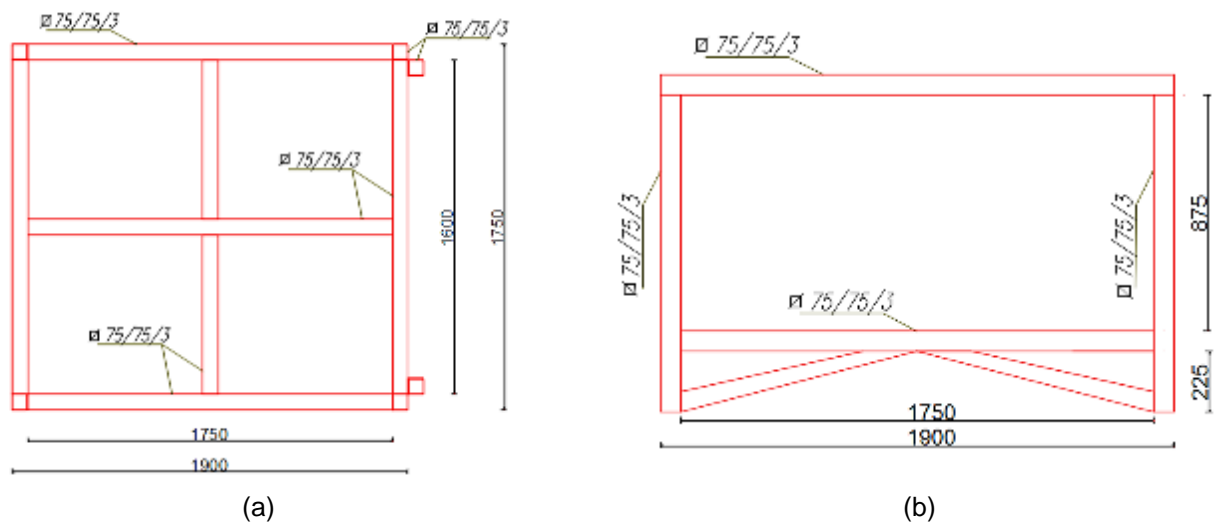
Esquema de una sección estructural. (a) Vista en planta de la estructura base. (b) Vista lateral de la estructura base. Fuente: elaboración propia.
